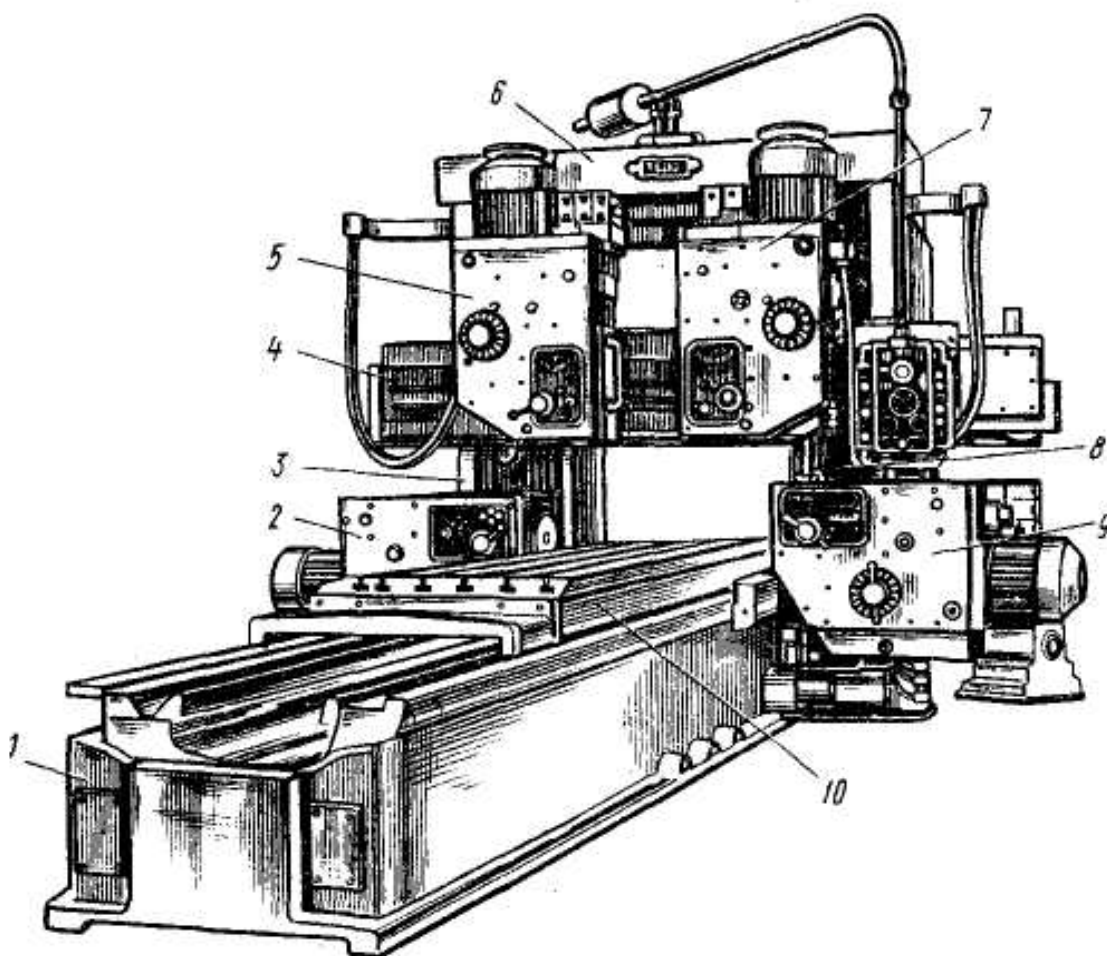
Продольно-фрезерный станок: 1 – станина; 2 – левая горизонтальная шпиндельная головка; 3 – левая стойка; 4 – траверса; 5 – левая вертикальная поворотная шпиндельная головка; 6 – балка; 7 – правая вертикальная поворотная шпиндельная головка; 8 – правая стойка; 9 – правая горизонтальная шпиндельная головка; 10 – стол
